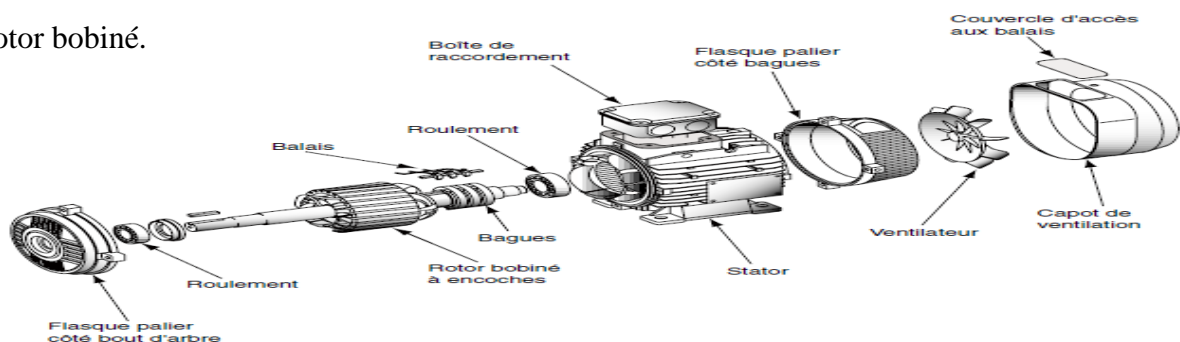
Différentes pièces d'un moteur asynchrone triphasé à rotor bobiné (À bagues).
